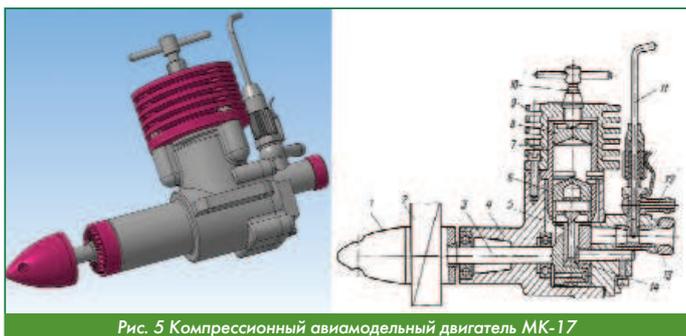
Компрессионный авиамодельный двигатель МК-17
